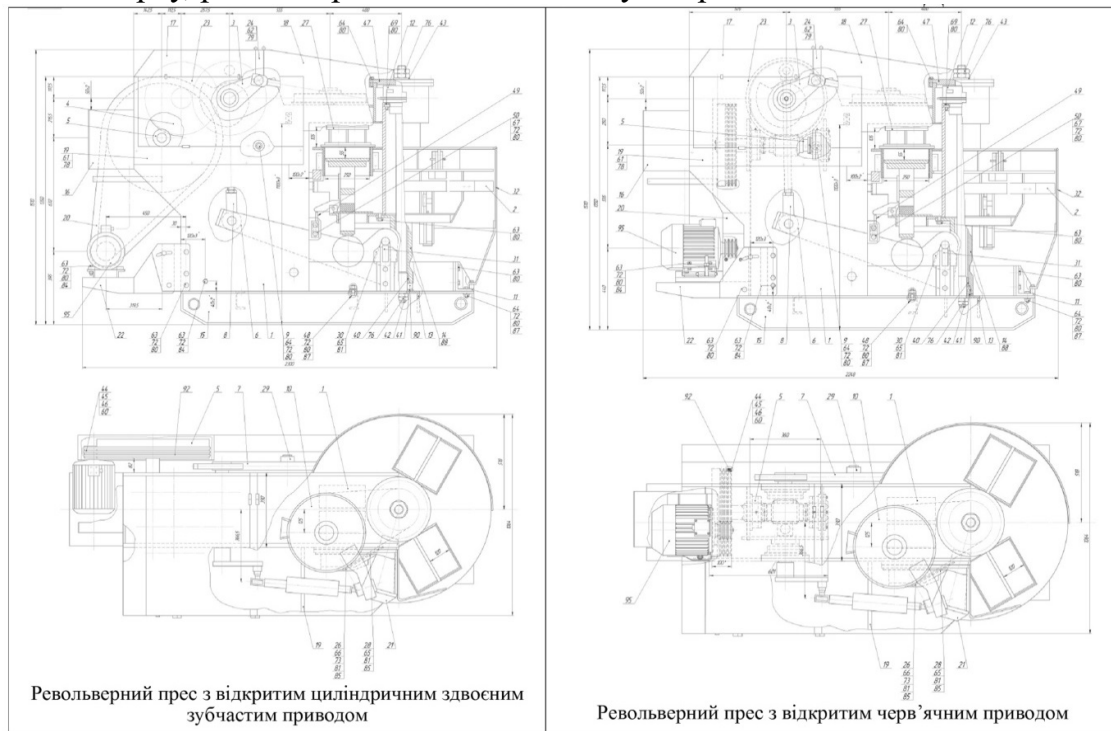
Вид загальний револьверного преса для формування напівфабрикатів керамічної цегли
